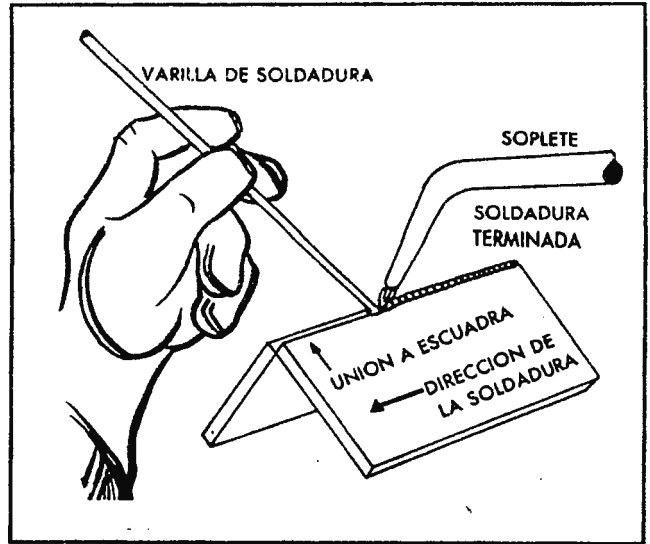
Soldadura a escuadra con varilla de soldadura
